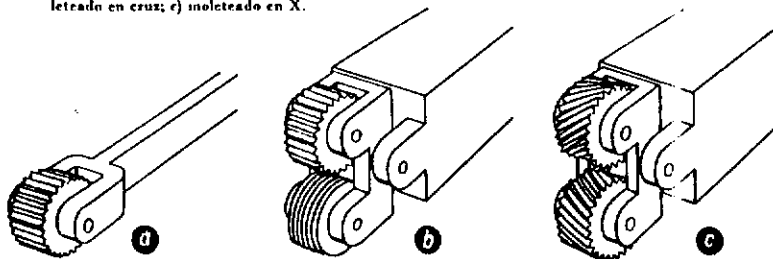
,2. Herramientas para molear: a) Rueda para moletado paralelo, con portaherramienta; b) Pareja de ruedas montadas para moletado en cruz, con portaherramienta; c) Pareja de ruedas para moletado en X, con portaherramienta.
